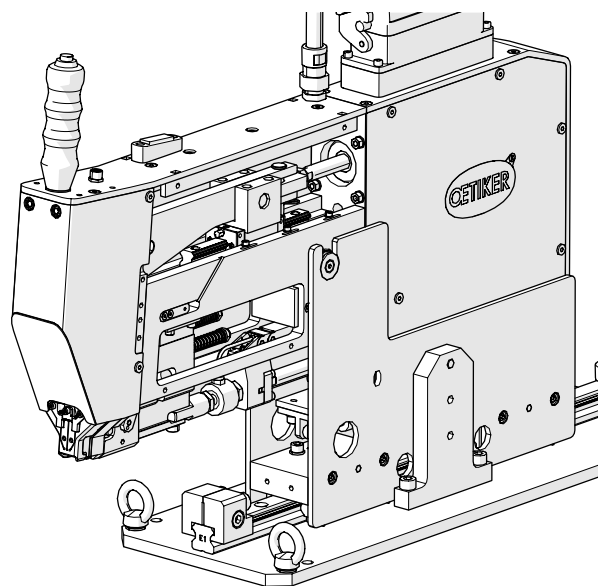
Werkzeug mit abgenommenen Frontabdeckungen
